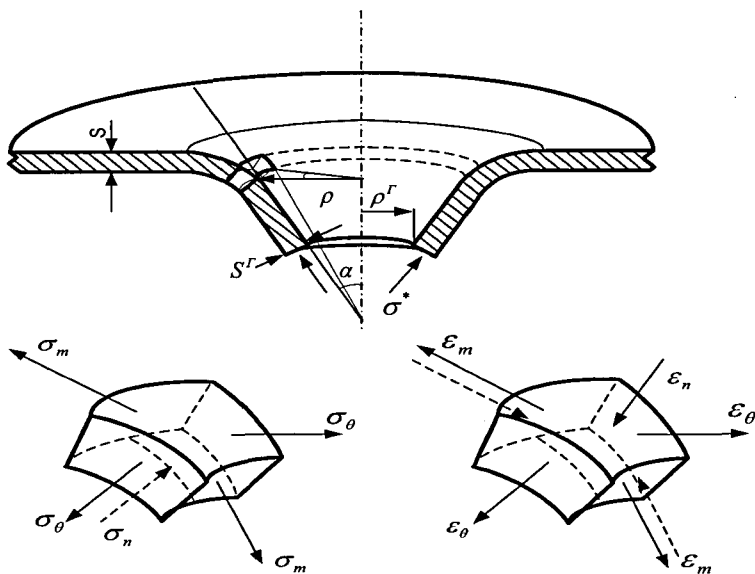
Схемы напряжений и деформаций при получении конической отбортовки отверстия
